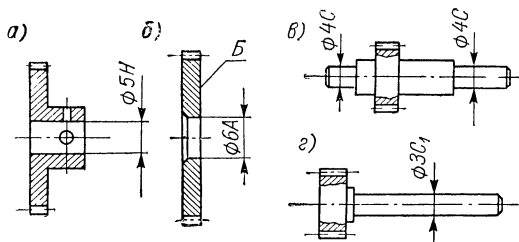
Базирующие поверхности и оси вращения зубчатых колес
